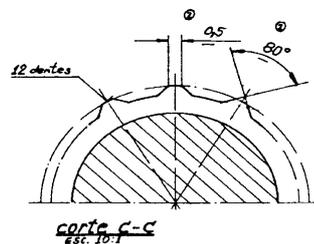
Primeiro tipo de perfil utilizado (projeto original).
